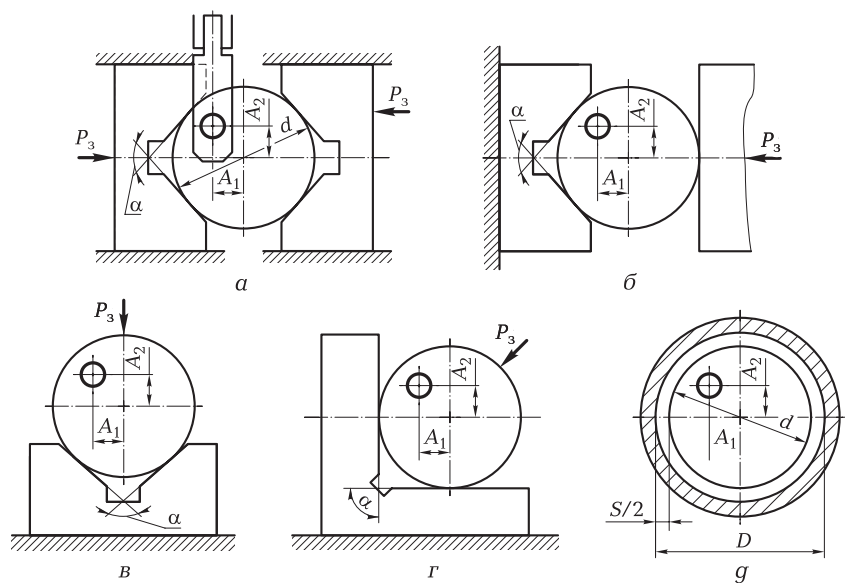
Схемы установки диска [P_3 — сила зажима заготовки]
